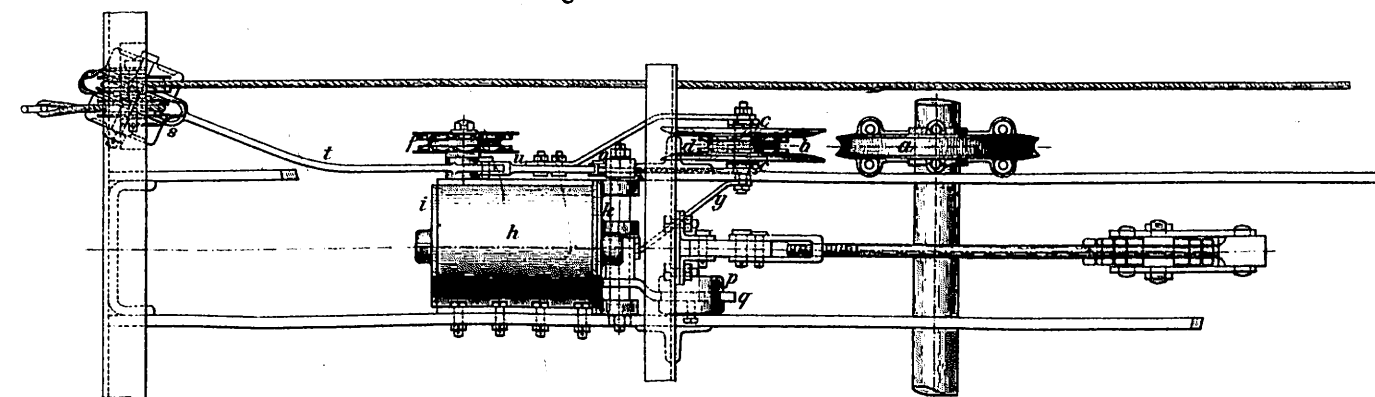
Grundriss. 1:15 d. nat. Gr.
